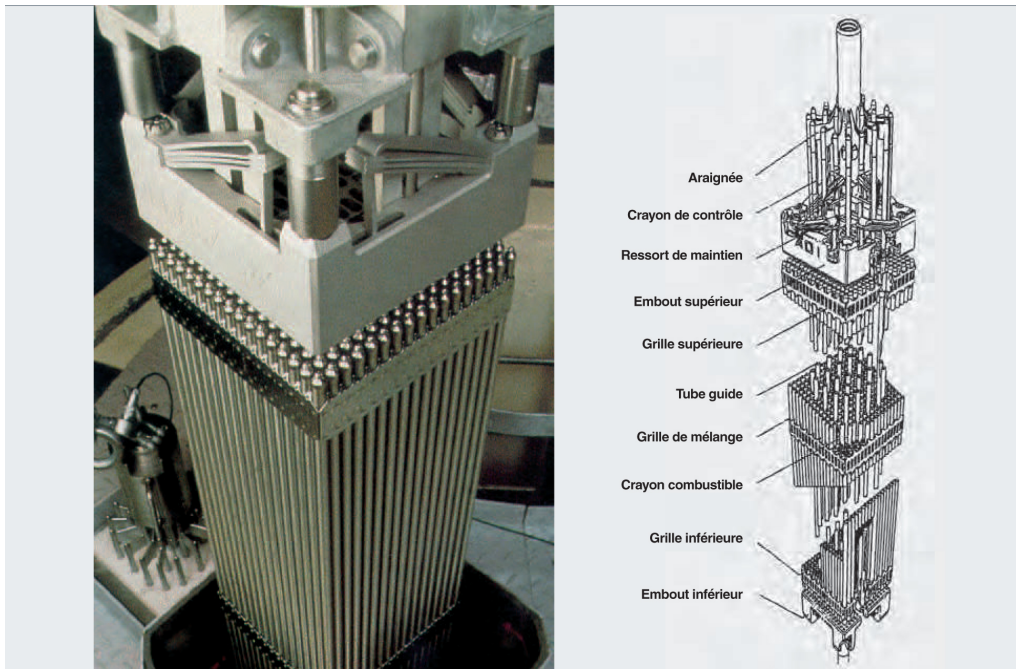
Vue éclatée d’un assemblage combustible.
